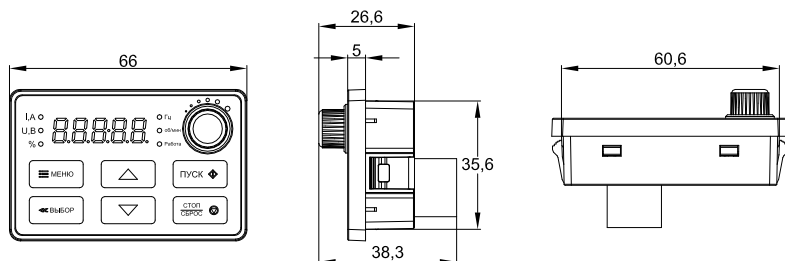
Габаритные размеры и размеры отверстий внешней цифровой однострочной панели управления (единица измерения – мм)
